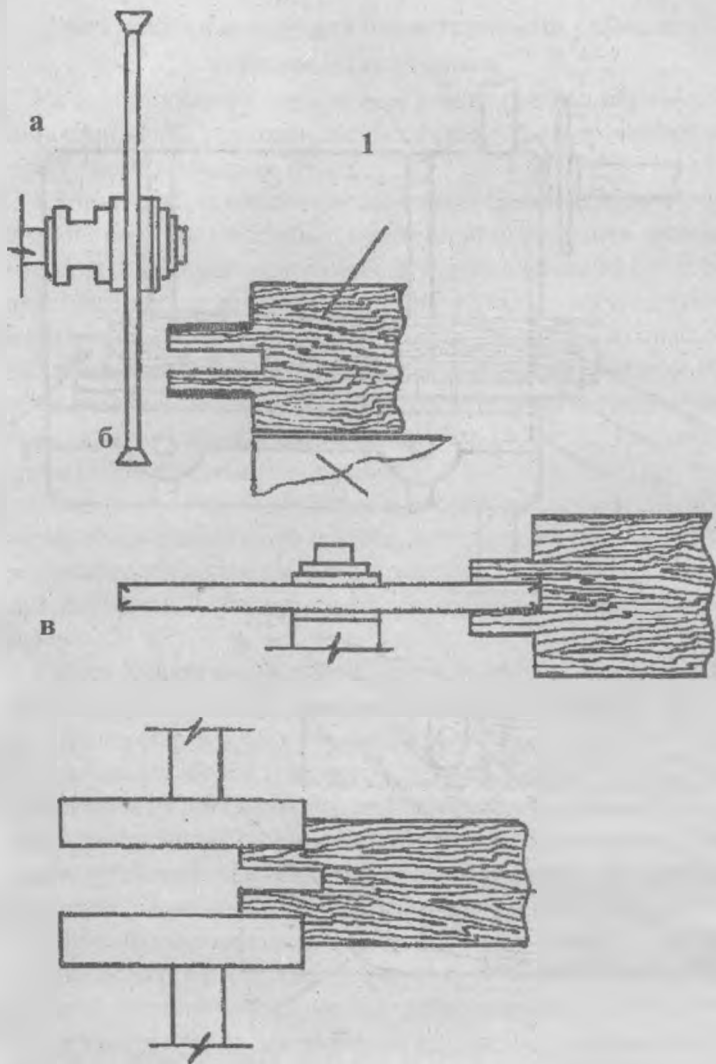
Настройка режущих инструментов шипорезного станка для рамных шипов:
